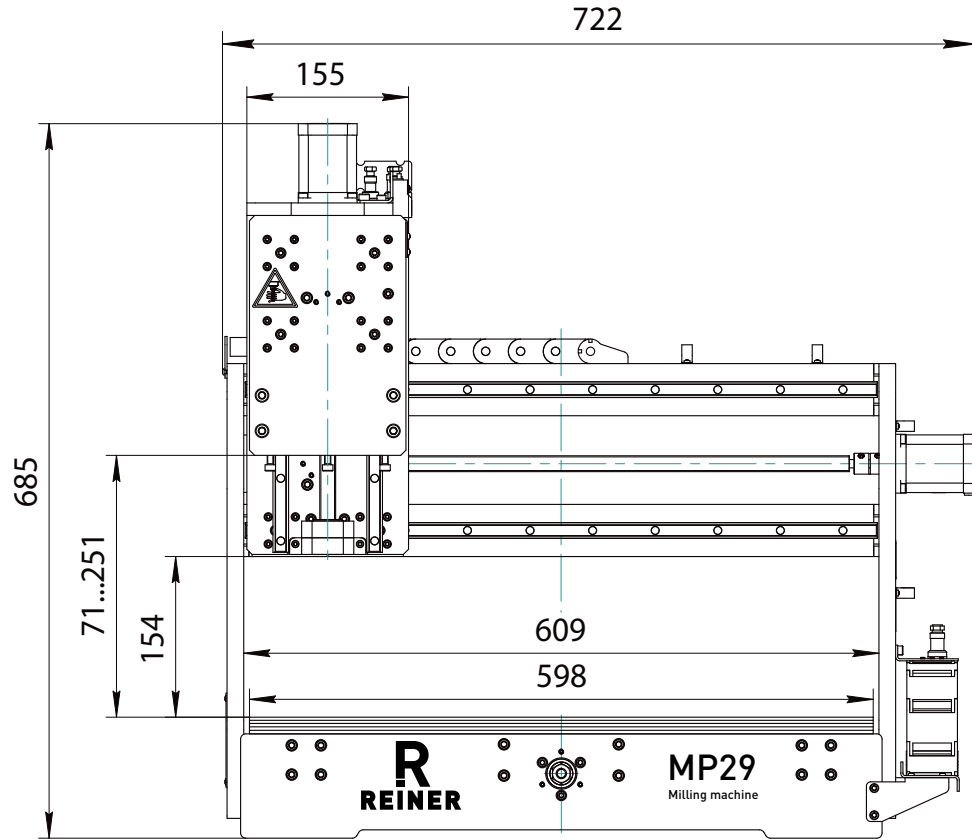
Габаритные и присоединительные размеры MP29.
